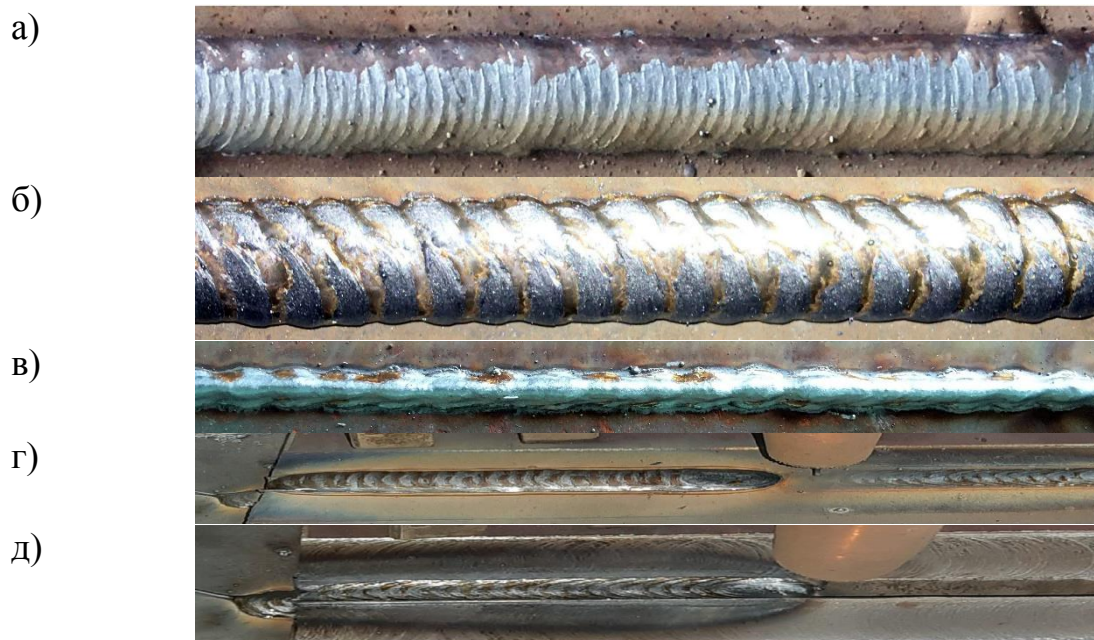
Образцы сварных швов листовых заготовок при различных типах перемещения сварочной горелки
